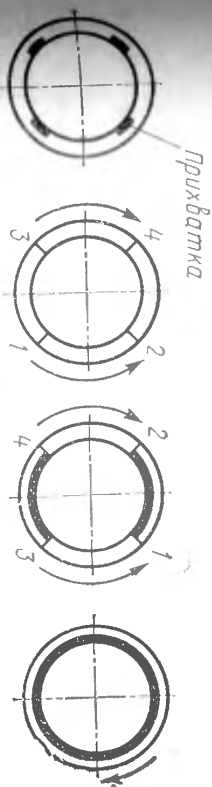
Порядок сварки поворотных стыков трубопроводов
